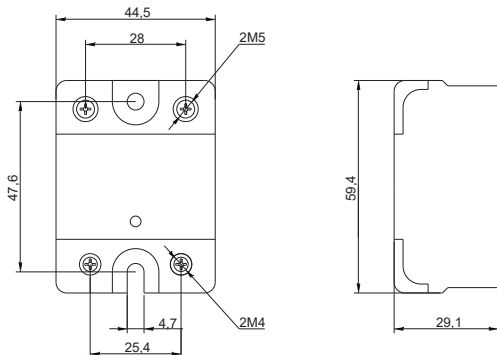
Габаритно-установочные размеры реле / Figure 1 – Overall and mounting dimensions of the relay / Сурет 1 – Реленің габариттік орнату өлшемдері
